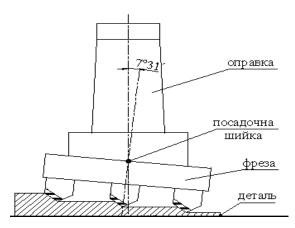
Схема прогресивного процесу фрезерування поверхні деталі
